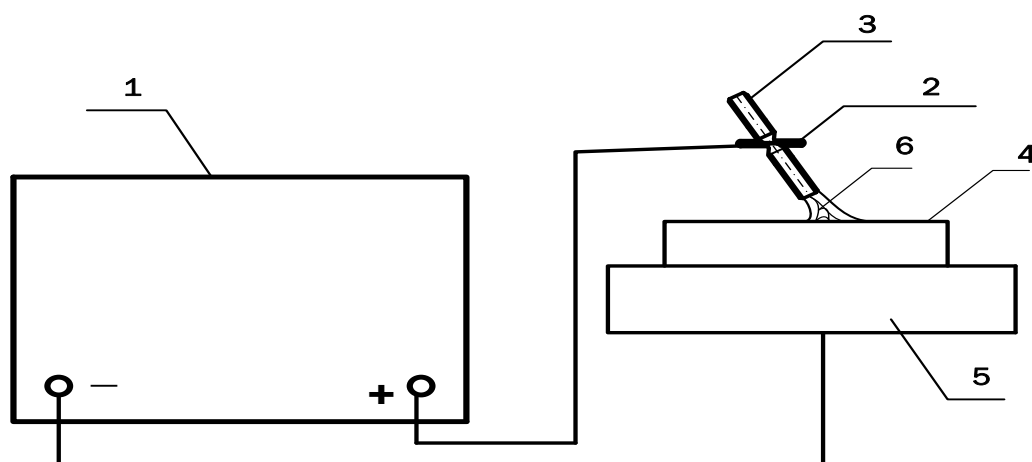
Схема сварки предлагаемым электродом
